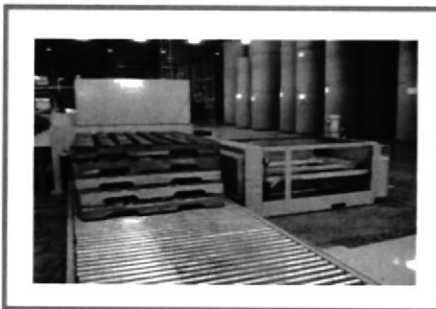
Detalle de las horquillas cuando levantan la pila de pallets (desde el segundo pallet para que el primero pase al load máster por medio del conveyor).
